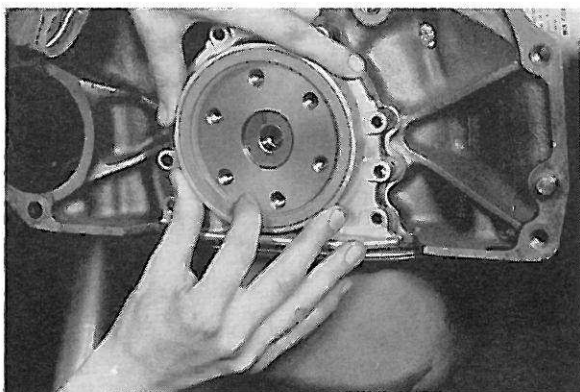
Montage de la bride d'étanchéité arrière (joint caoutchouc)
